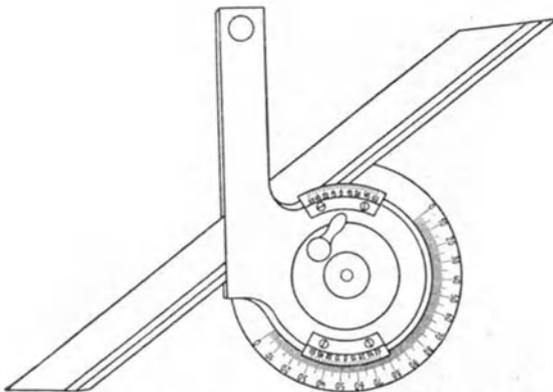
Donauwerk Ernst Krause u. Co., Wien.
